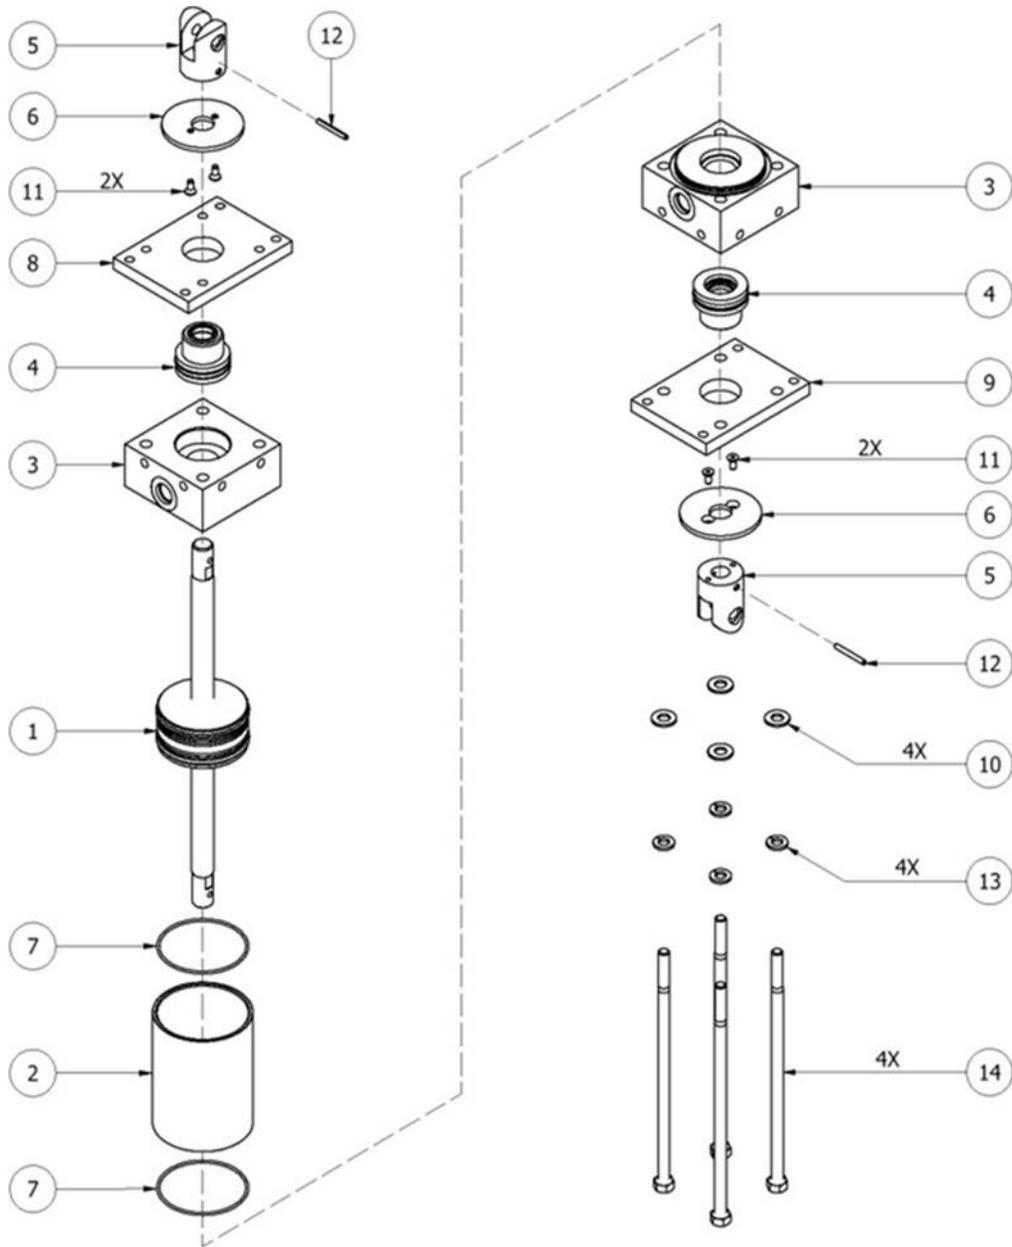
Ensamblaje del cilindro hidráulico (HI-05336)
